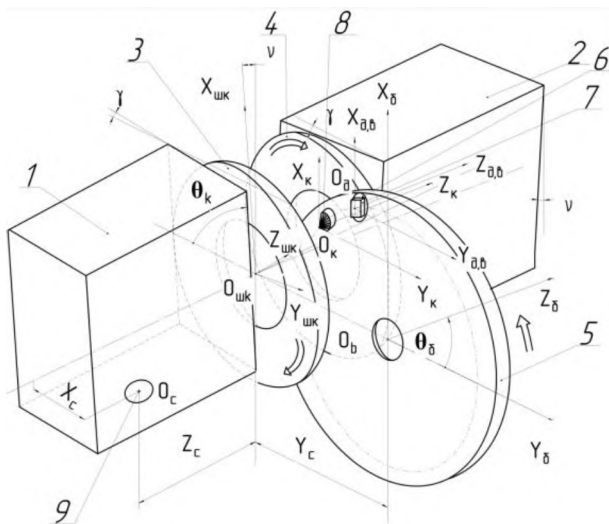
Розрахункова схема формоутворення торців циліндричних деталей з некруглим профілем
